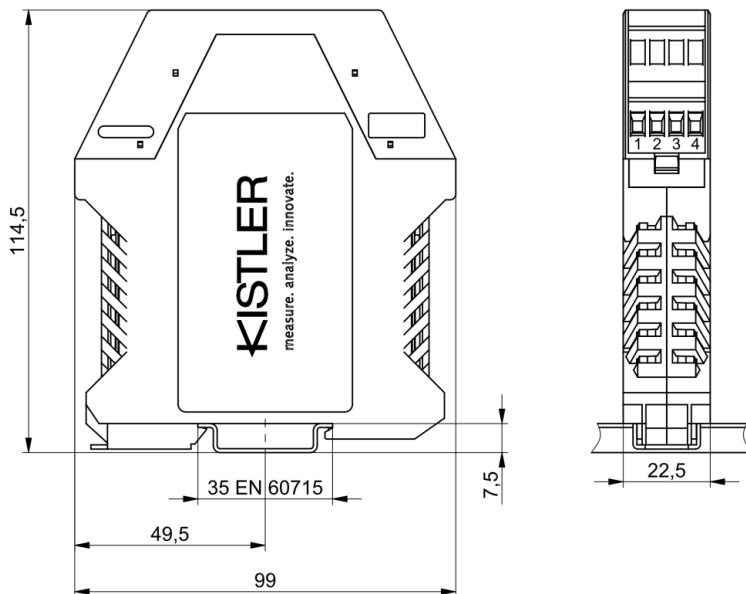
Dimensionen des differenziellen Ladungsverstärkers in Kunststoff DIN-Schienen Gehäuse Ausführung
